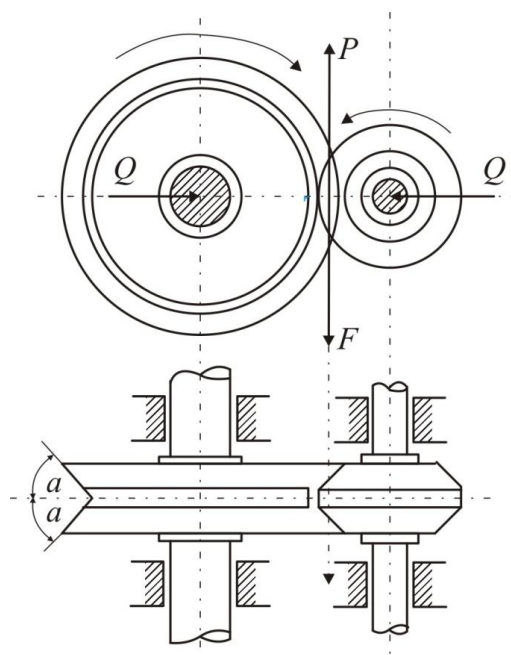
Схема передачи с фрикционными клинчатыми колесами
